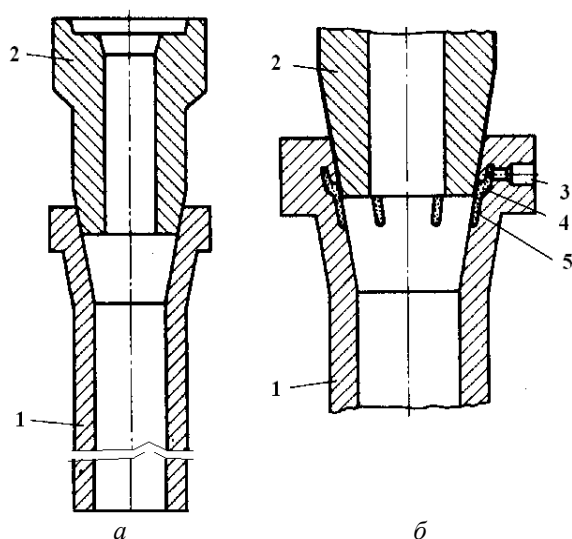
Установка защитной трубы сталеразливочного ковша:
